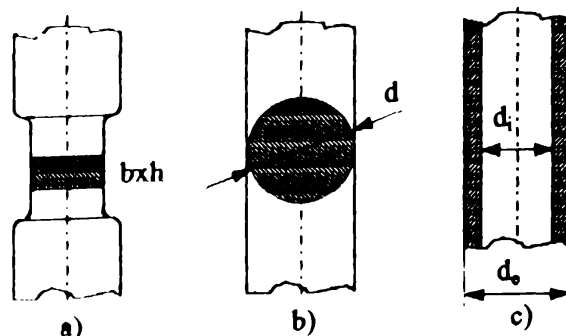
Secțiune transversală în zona de lipire a timbrelor tensometrice pe bara de măsurare
